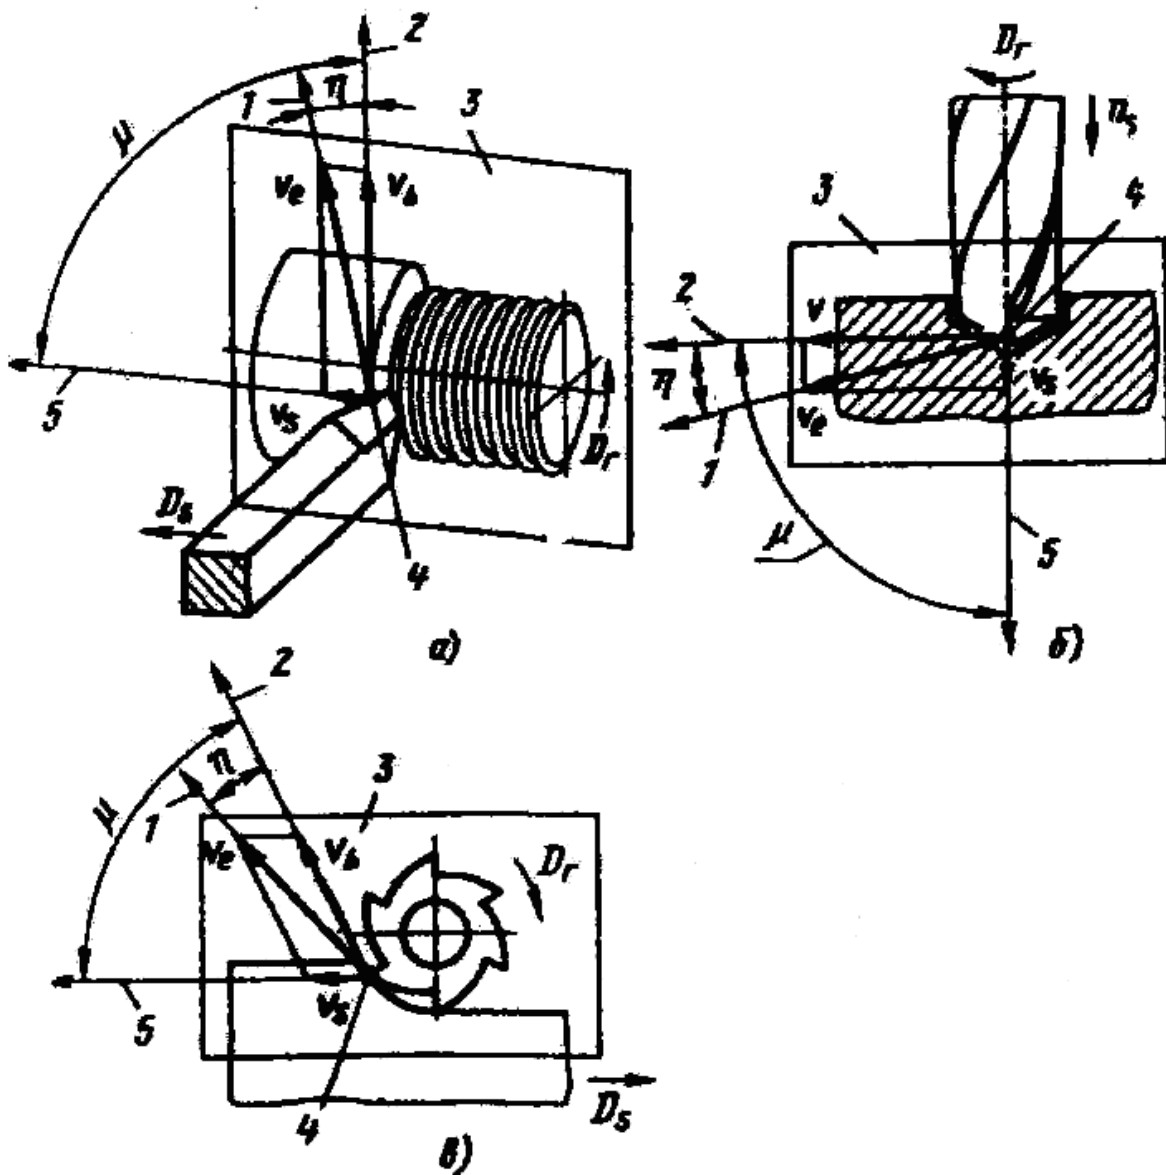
Элементы движений в процессе резания при обтачивании (а), сверлении (б) и фрезеровании (в):
